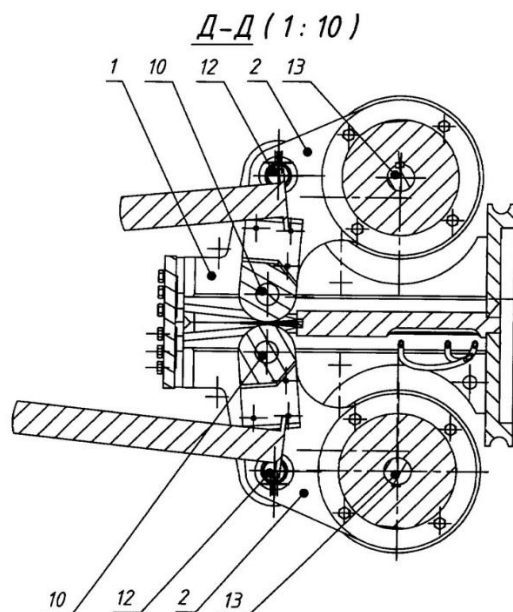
Механизм перемещения машины для сварки труб, в дальнейшем "механизм перемещения", сечение Д-Д
